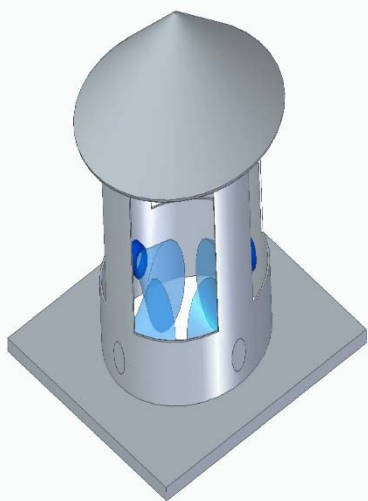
esempio di flangia precedentemente predisposta misura 30 cm di diametro per 20 cm di altezza, con installato impianto di brumizzazione
